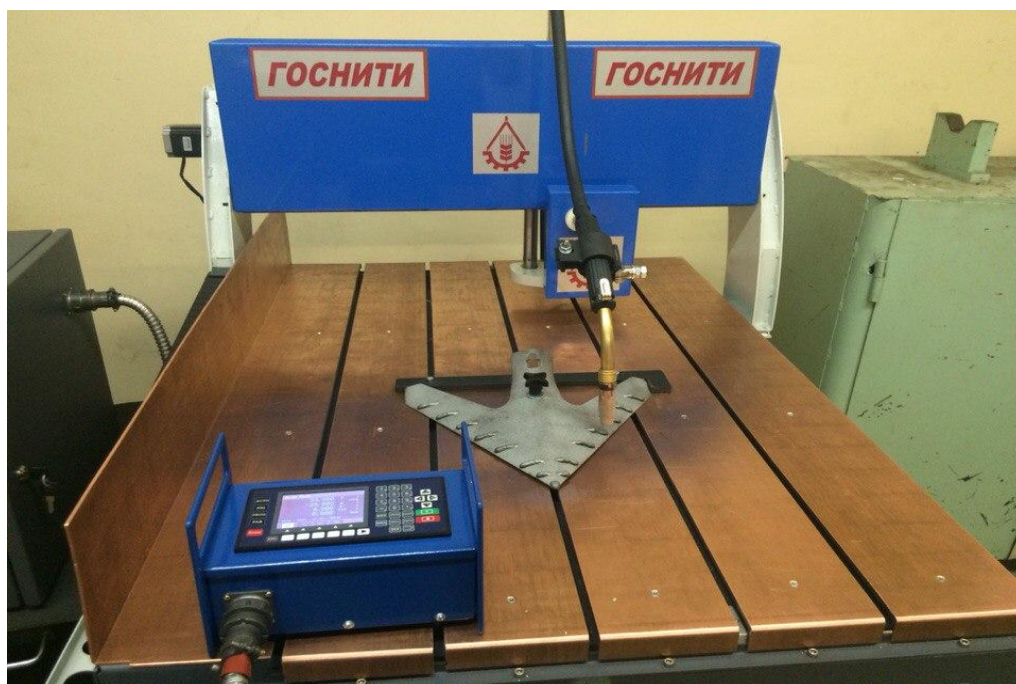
Установка для упрочнения деталей электродуговой наплавкой [2]
